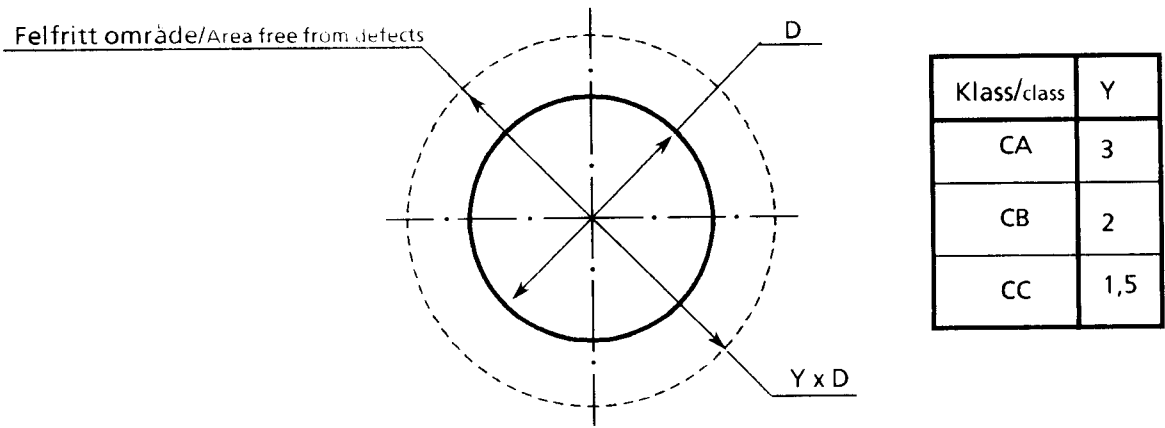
Yttre defekter i borrhål i snittad (bearbetad) yta/External defects in drilled (machined) hole in sectioned area
